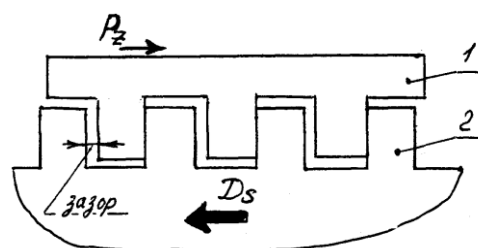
Схема выборки зазора в винтовой передаче при встречном фрезеровании; 1 – гайка стола; 2 – ходовой винт
